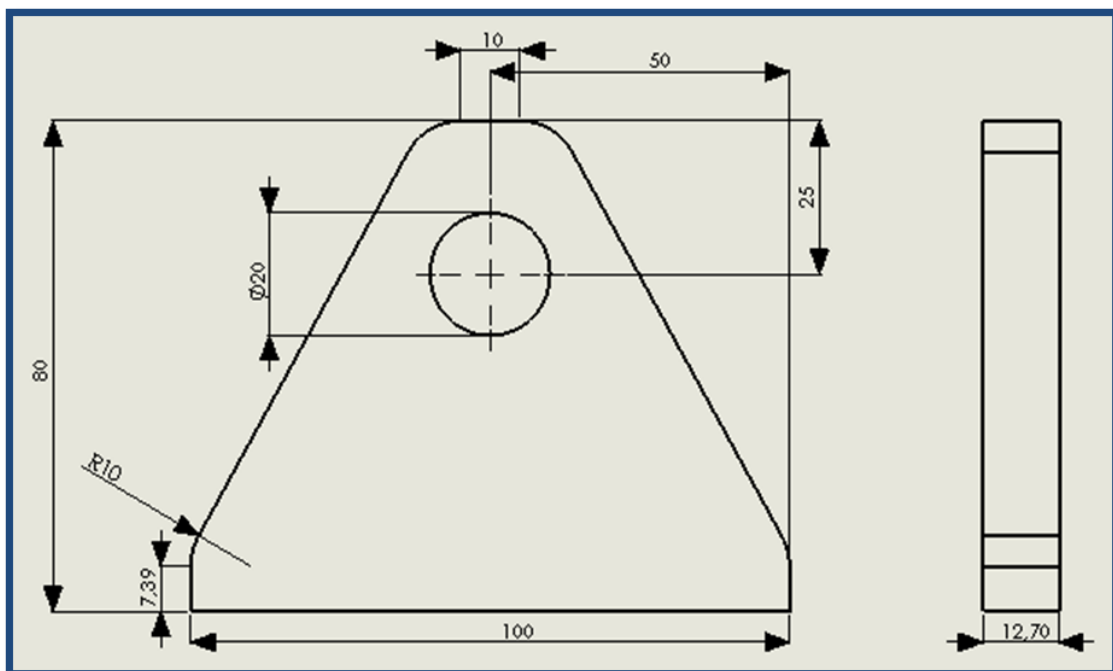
Dimensiones del ojo para sostén del cilindro.
